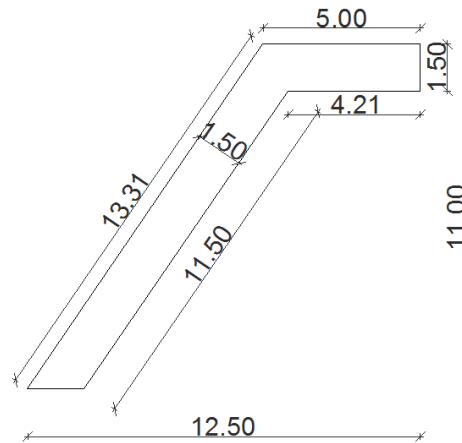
Soporte para estructura. Plano para soporte de estructura del cuadricóptero con medidas en centímetros.
